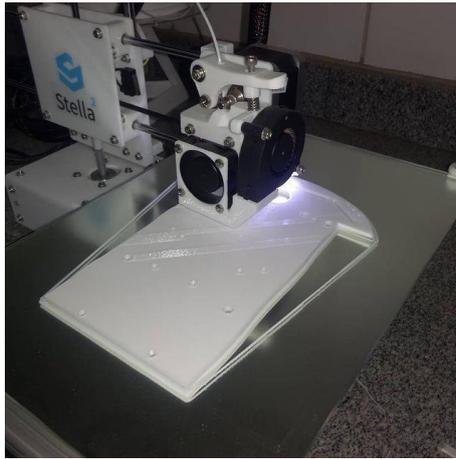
Impressora 3D durante o processo de deposição de filamento PLA pela técnica FDM.
